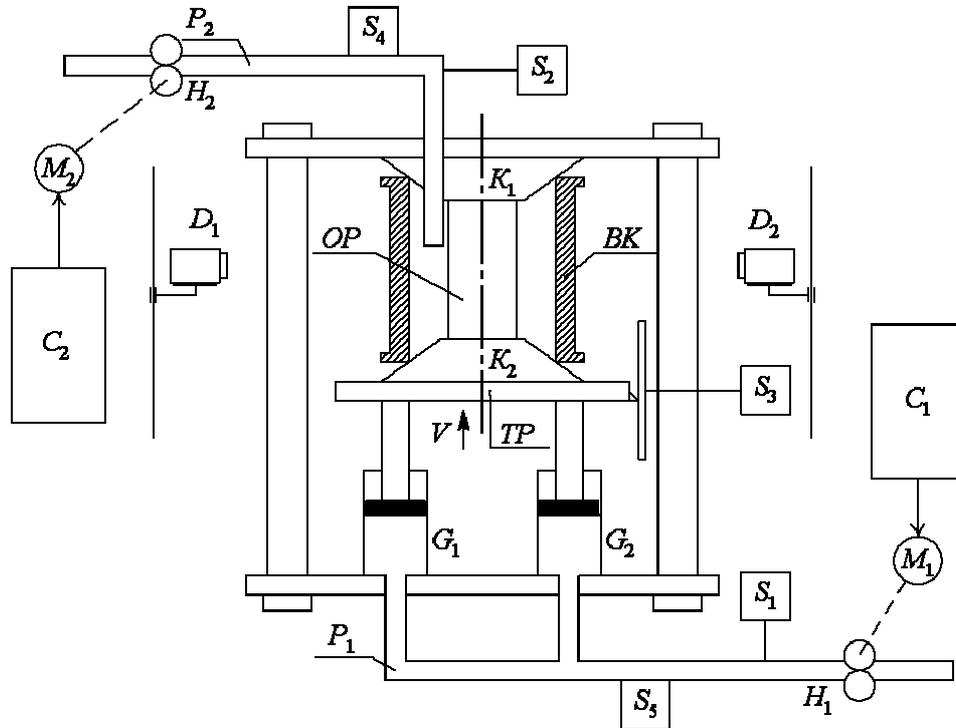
Процесс гидрорастяжения кольцевой заготовки на вертикальном прессе усилием 300 МН
